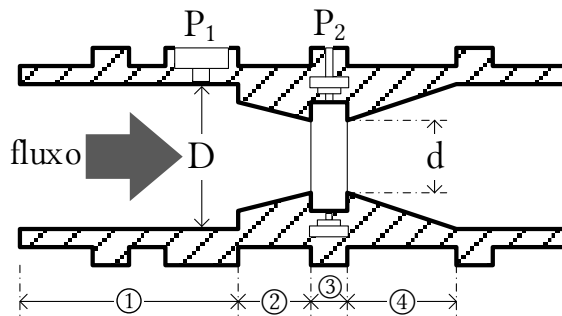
Medidor de vazão tipo tubo Dall. (1) cilindro de entrada; (2) convergente; (3) garganta; e (4) divergente.
